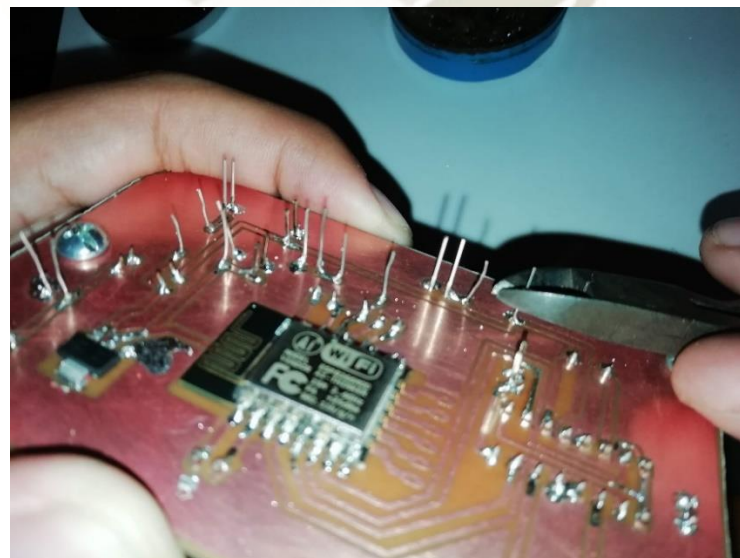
Eliminación de sobrantes en la soldadura
